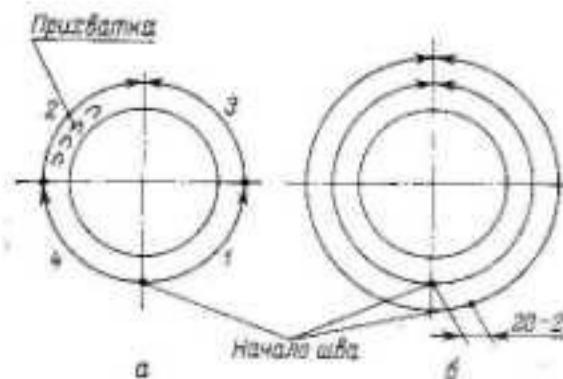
Последовательность сварки неповоротного стыка:
